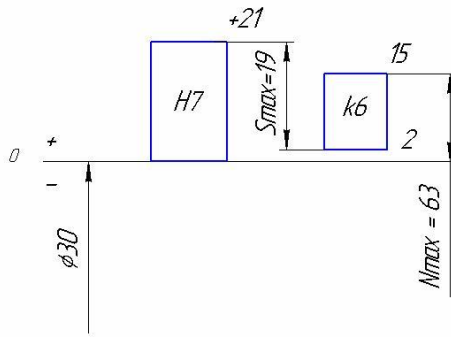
Схема расположения полей допусков деталей сопряжения
